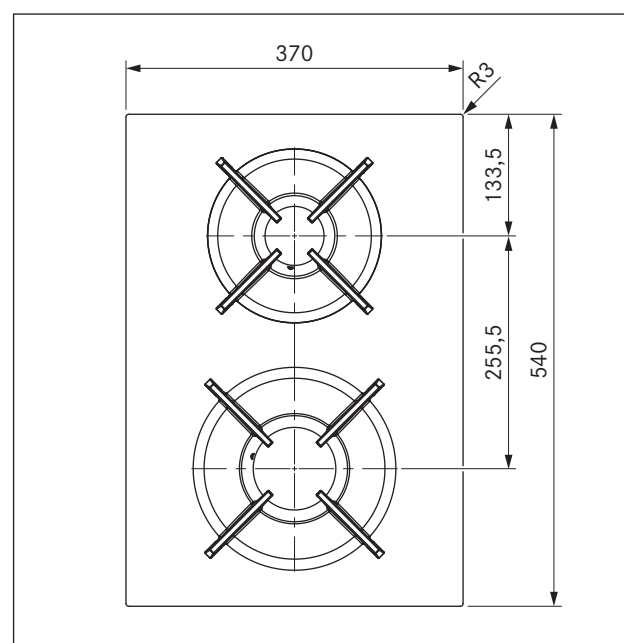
Dimensions PKG11 - Vue de dessus
